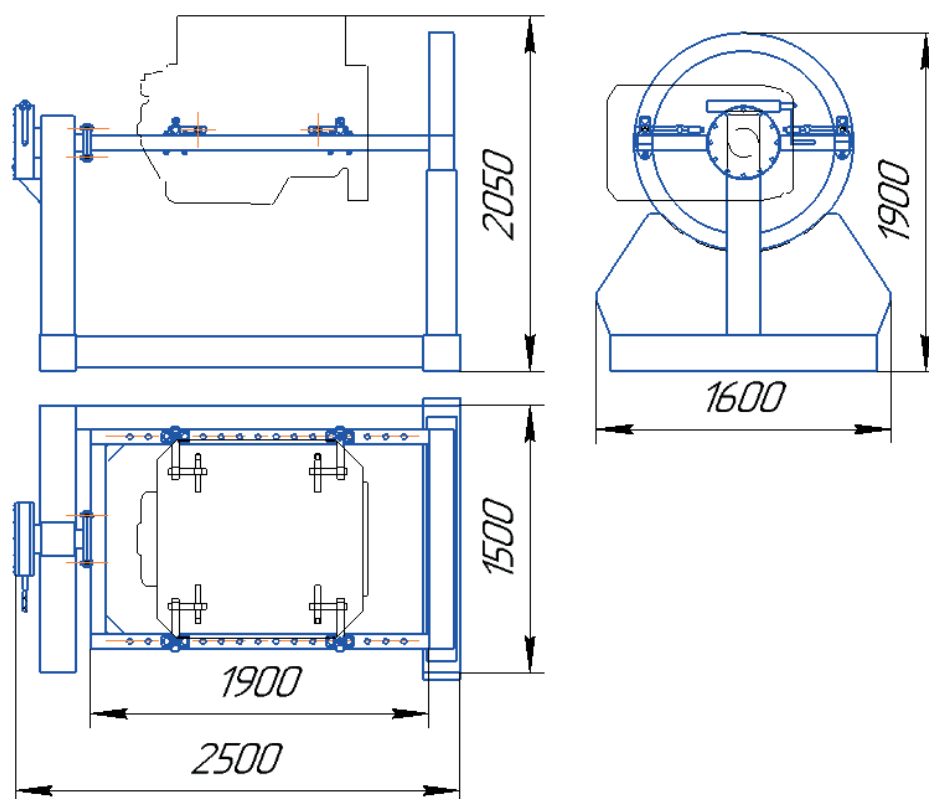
Общий вид модернизированного стенда для разборки и сборки двигателей и агрегатов
